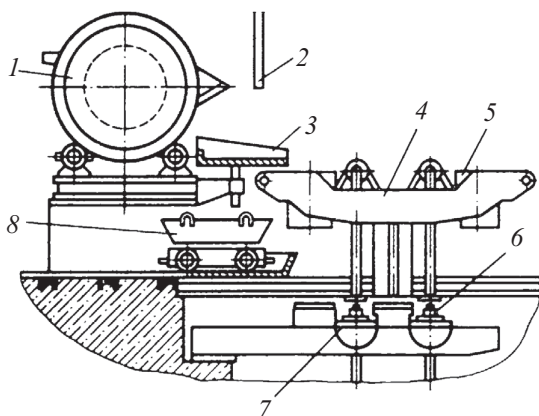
Ковшовая заливочная машина в комплекте с миксером, обогреваемым газом: 1 – миксер; 2 – ограждение; 3 – лоток; 4 – поворотная рама; 5 – ковш; 6 – гидроцилиндр поворота ковша; 7 – гидроцилиндр для механизации слива остатков расплава; 8 – изложница
